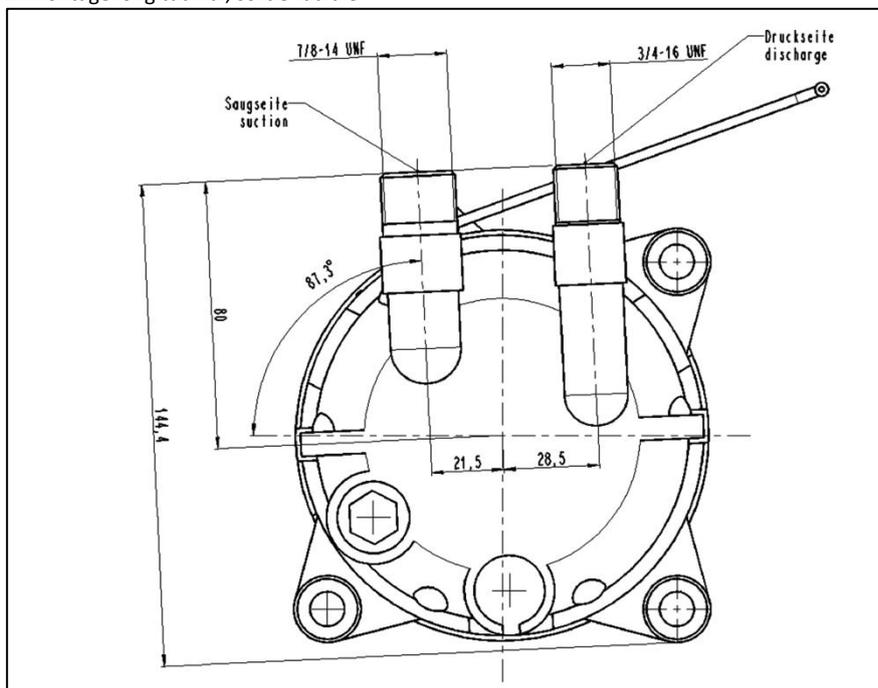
Cotes de raccordement pour un montage longitudinal
